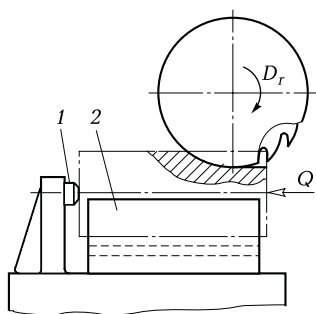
Установка и закрепление валика при фрезеровании:
